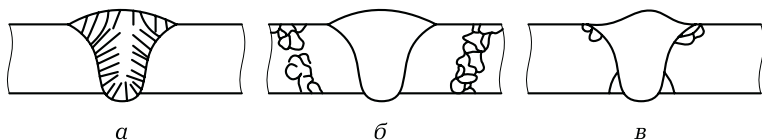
Схемы межкристаллитной коррозии сварных соединений аустенитных сталей:
